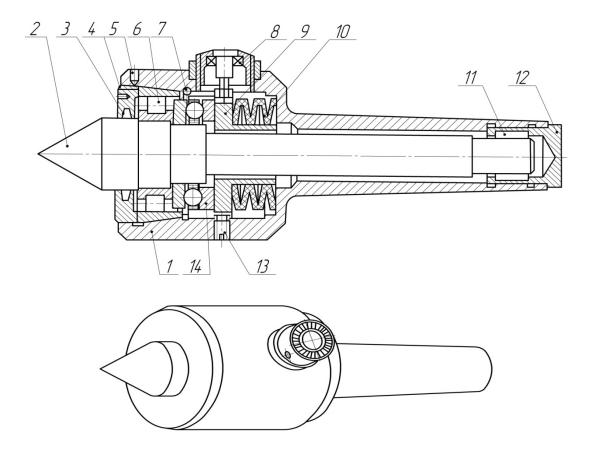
Вращающийся центр с указателем осевого усилия: 1 — корпус; 2 — центр; 3 — сальник; 4 — гайка; 5, 13 — винты; 6 — роликовый подшипник; 7 — кольцо; 8 — указатель осевого усилия; 9 — фланец; 10 — пружина; 11 — игольчатый подшипник; 12 — заглушка; 14 — шариковый упорный подшипник
